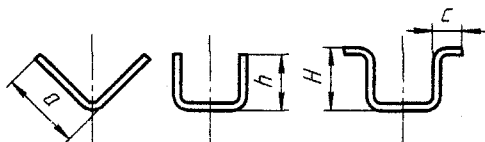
Схемы конструкций гнутых изделий:
